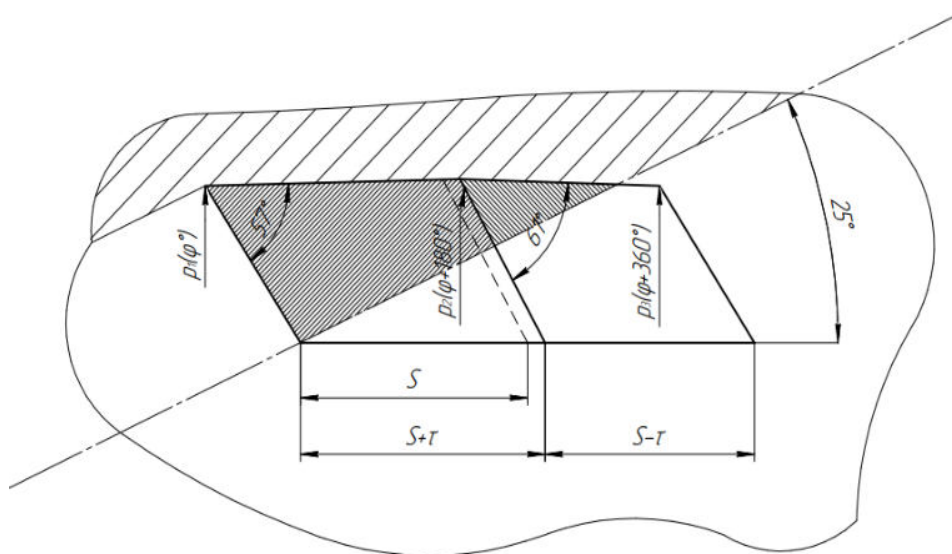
Схема формирования площадей срезаемых сечений припуска для сверла диаметром 2 мм, при S_{max}
